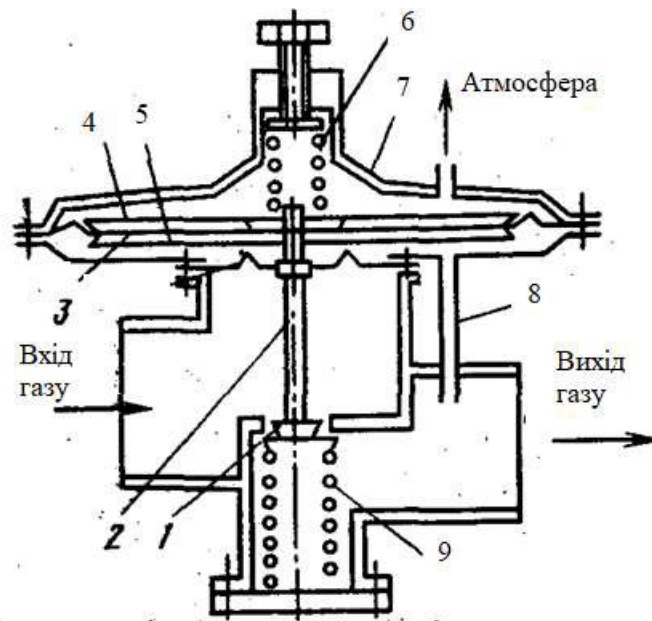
Регулятор тиску газу: 1 – редукційний клапан; 2 – шток; 3 – керуюча діафрагма; 4, 5 – диски; 6, 9 – пружина; 7 – корпус; 8 – трубка
